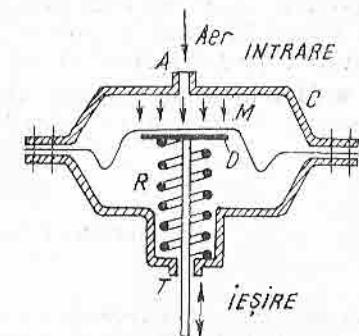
Motor de execuție pneumatic cu membrană.
